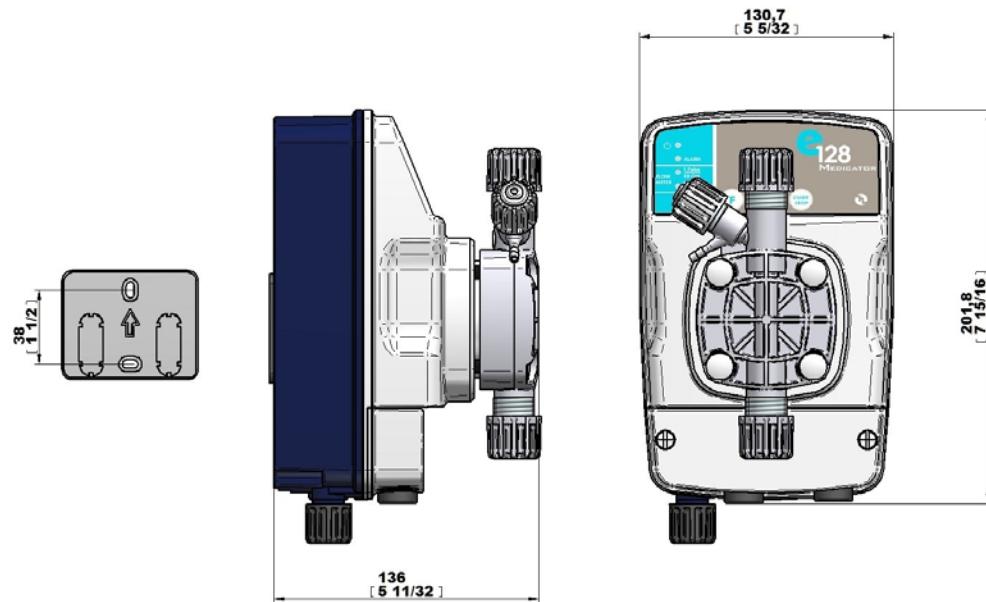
Dimensões em mm. Placa para montagem na parede.
